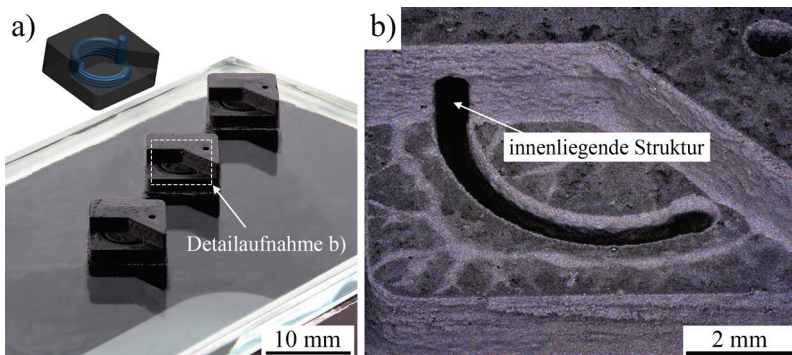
Prototyp eines WC-Co-Modellkörpers mit komplexer innenliegender Struktur. Zur Darstellung der inneren Strukturen wurde der Prototyp teilweise geöffnet gedruckt; siehe auch [36].
